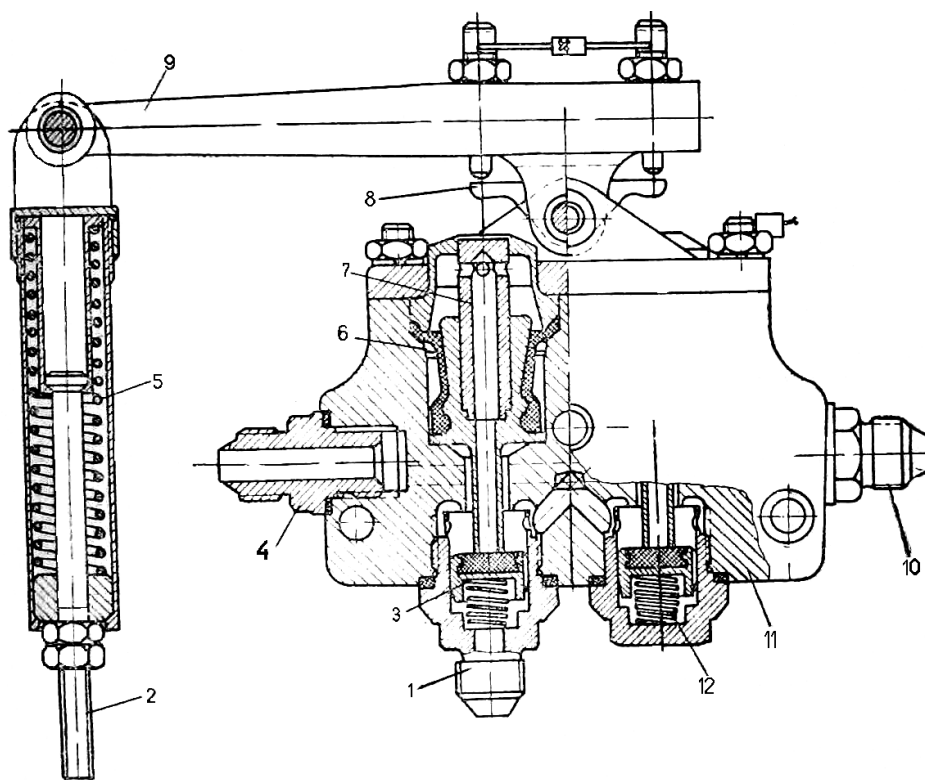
Редукционный клапан У139 (ПУ-7)
